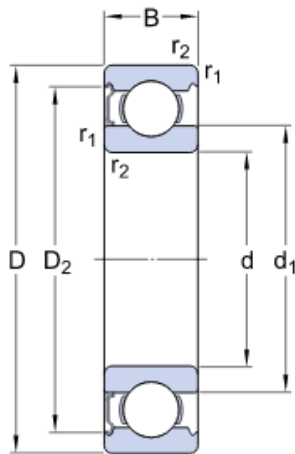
SKF 608-Z, rodamiento axial. (Bearing)
